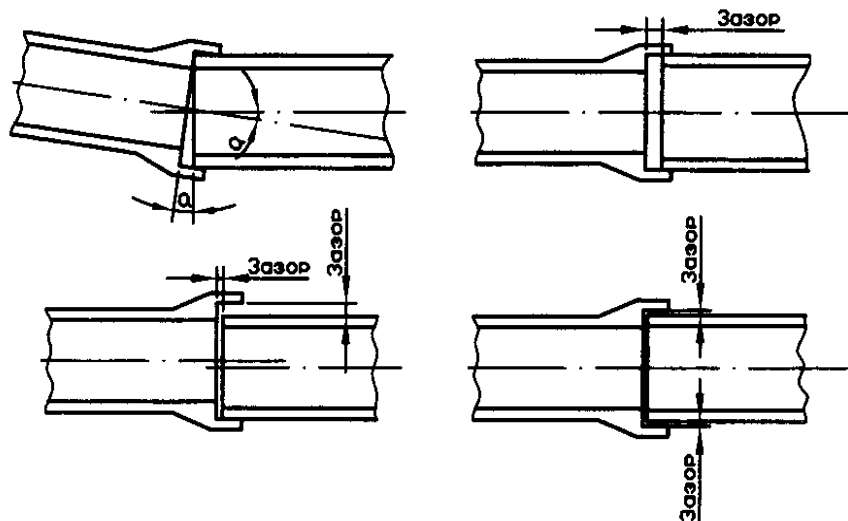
Виды дефектных соединений при раструбной или раструбно-стыковой сварке
